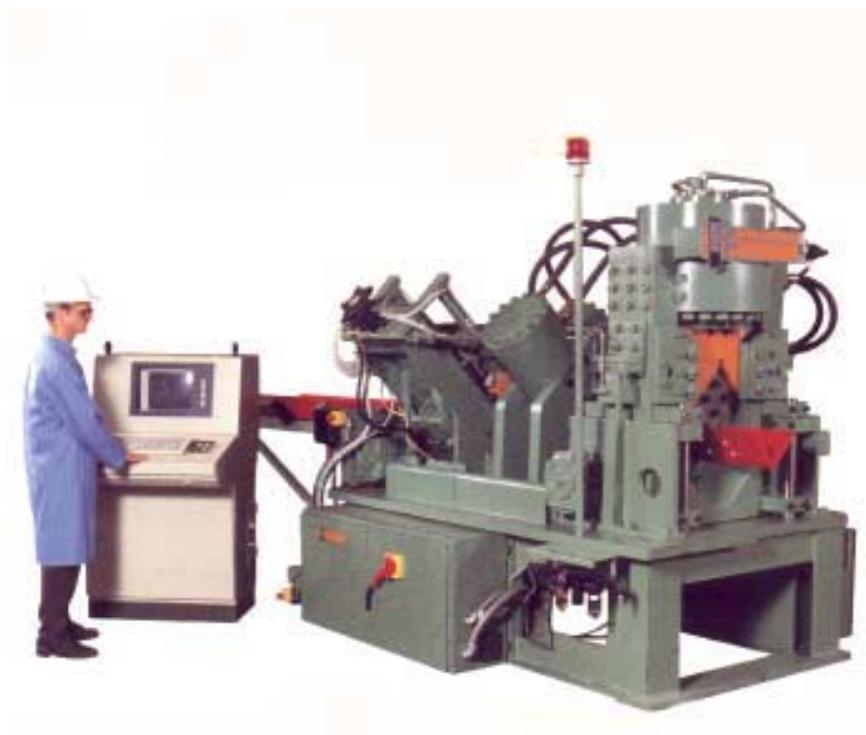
Máquina CNC para preparação de perfis U, C e chapas.
